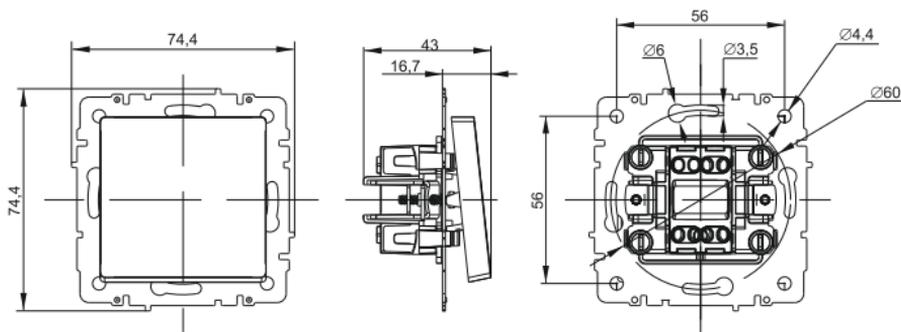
Габаритные и установочные размеры выключателей без рамки / Figure 2 – Overall and mounting dimensions of switches without frame / 2-сურет-Жақтауы жоқ ажыратқыштардың габаритті және орнату өлшемдері / Figura 2 – Dimensiunile și dimensiunile de instalarea a comutatoarelor fără cadru / ნახატი 2 – ჩარჩოს გარეშე ამომრთველის გაბარიტული და საყენებელი ზომები / 2-сурет – Алкасыз өчүргүчтөрдүн көлөм жана орнотуу өлчөмдөрү / Расми 2-Андозаҳои умумӣ ва насбии калидакҳои бе ҷаҳорҷӯба / 2-rasm – Freymsiz viklyuchatelarning gabaritli va o'rnatishdagi o'lchamlari
